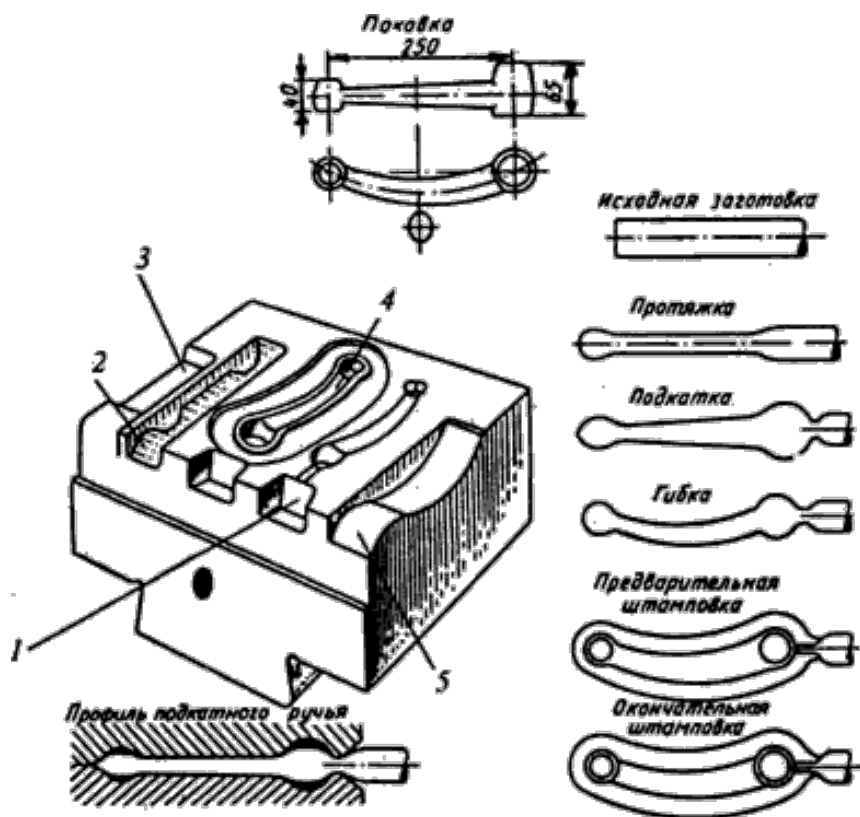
Стадии получения сложной поковки в нескольких ручьях:
